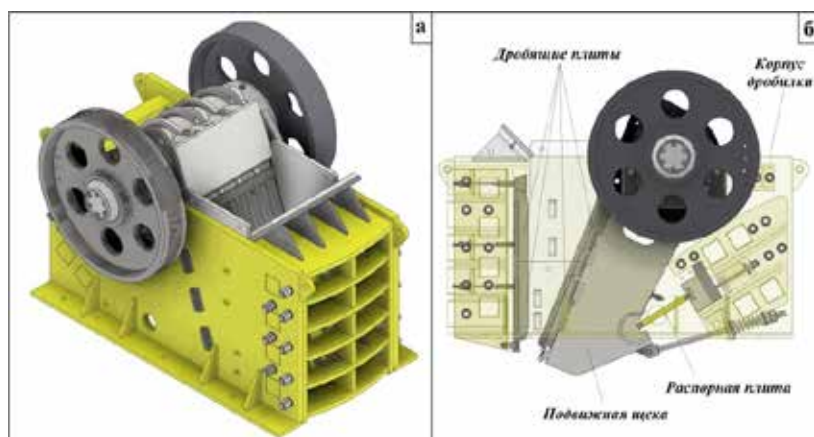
Общий вид дробилки PE 1200x1500 (а), конструктивная схема дробилки (б)
